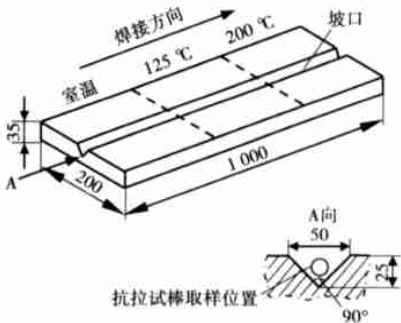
焊件结构与尺寸及取样位置(mm)
